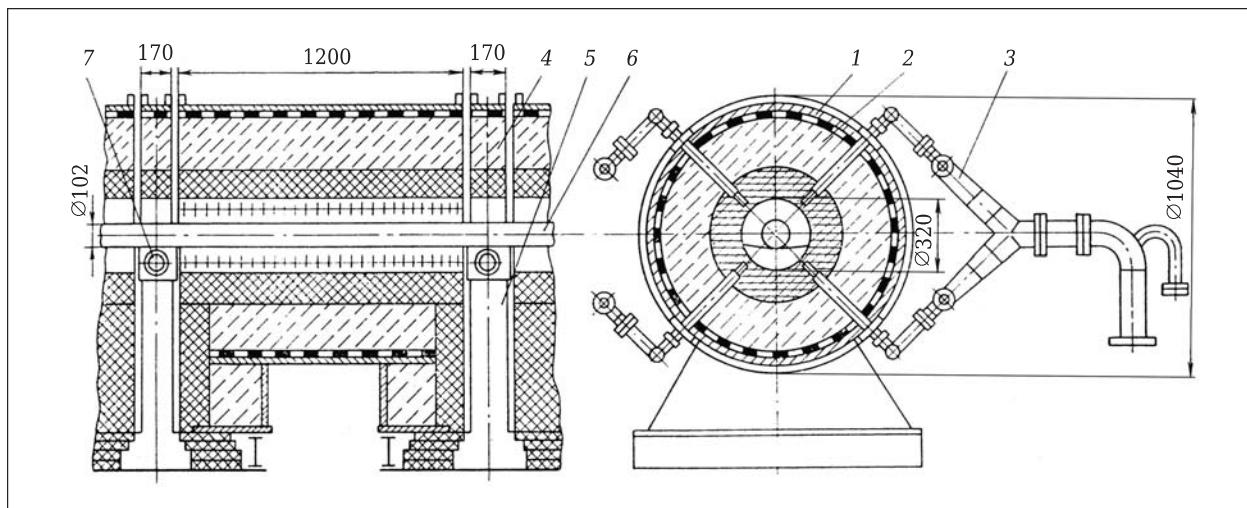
Секция одноручьевой печи СФН: 1 — корпус; 2 — кладка; 3 — многосопловая струйно-факельная горелка; 4 — крышка тамбура; 5 — дымоход; 6 — нагреваемая труба; 7 — транспортирующий ролик
